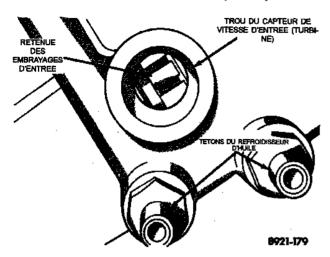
Vue à travers le trou du capteur de vitesse d'entrée
